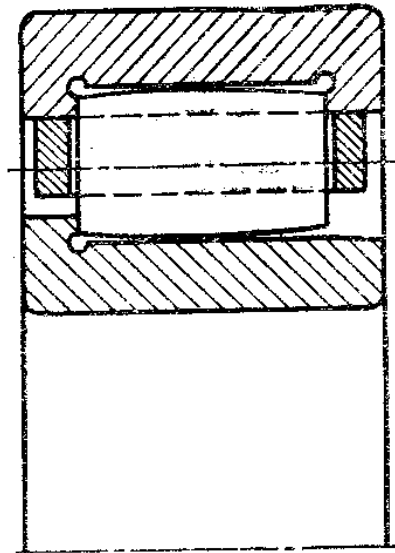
Роликопідшипник з короткими циліндричними бомбінованими роликами
